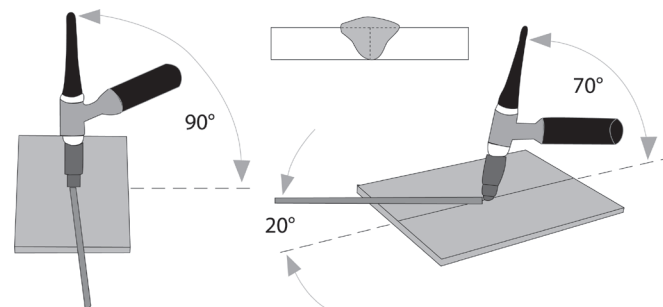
Положення «TIG»-пальника під час виконання зварювання стикового з'єднання.
